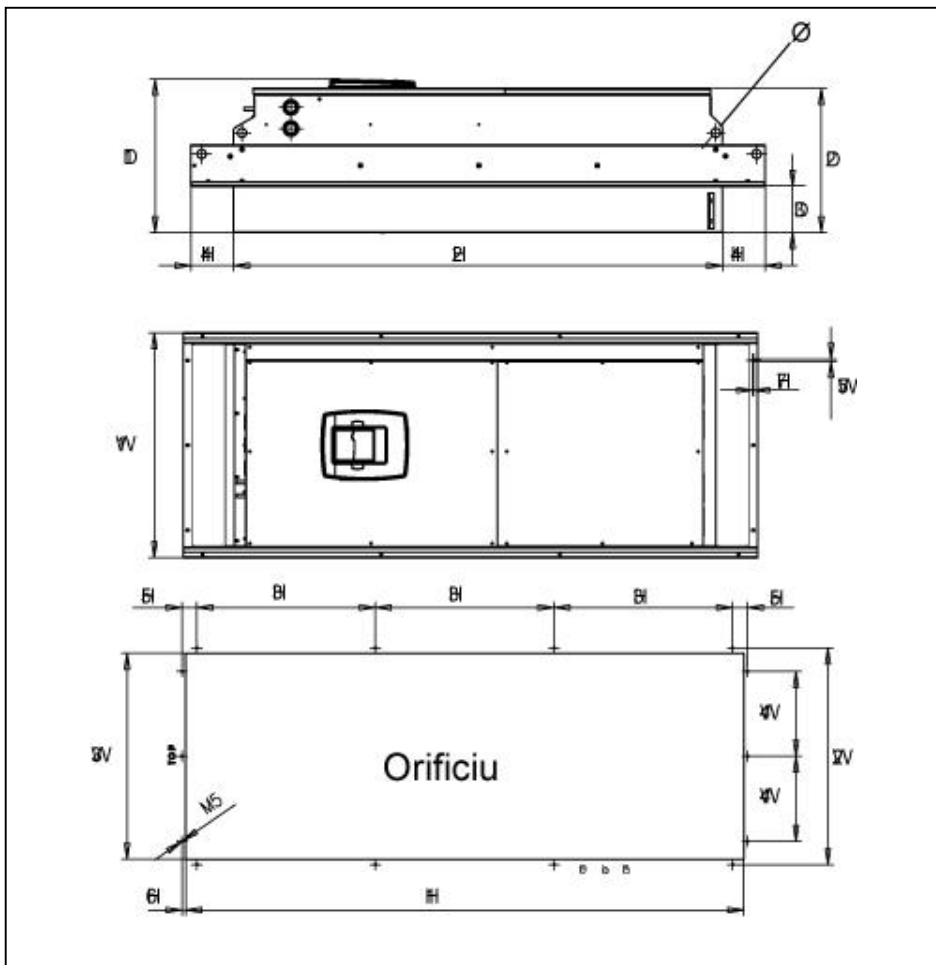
Dimensiuni Vacon NX\_. Montare cu flanșă pentru FR9
